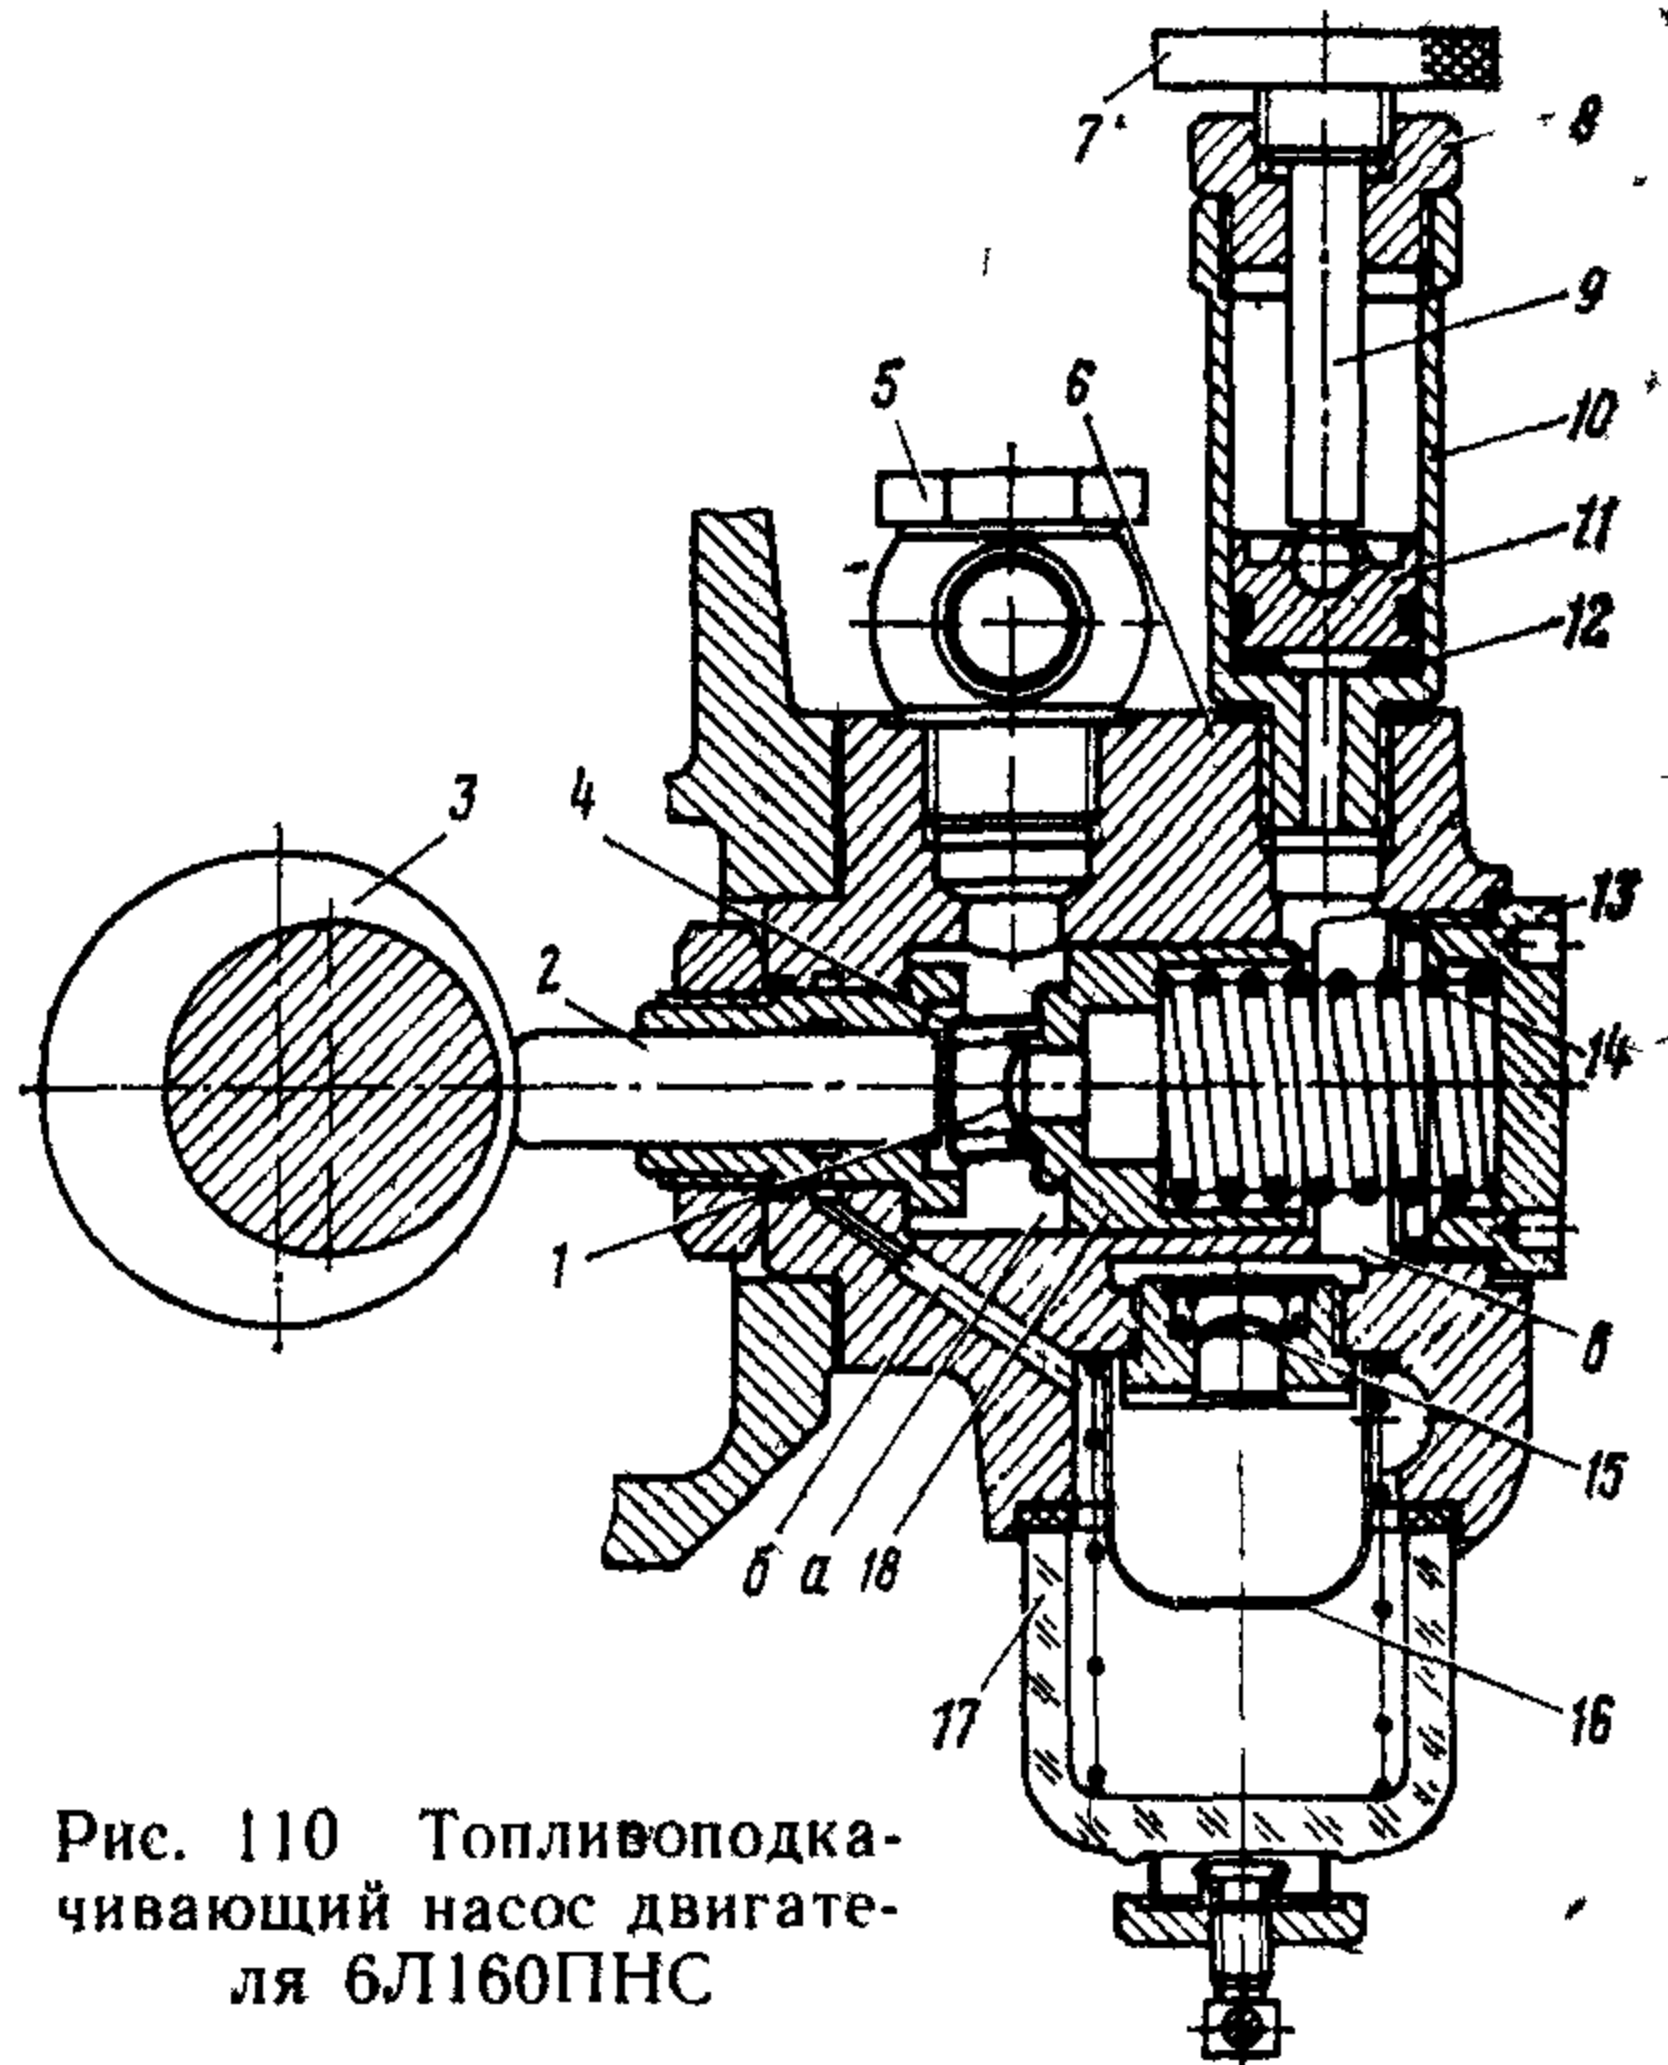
Топливоподкачивающий насос двигателя 6Л160ПНС
